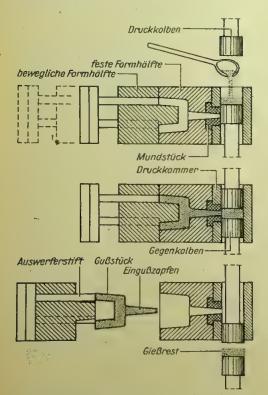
Druckgußverfahren mit senkrechter Kaltkammer
